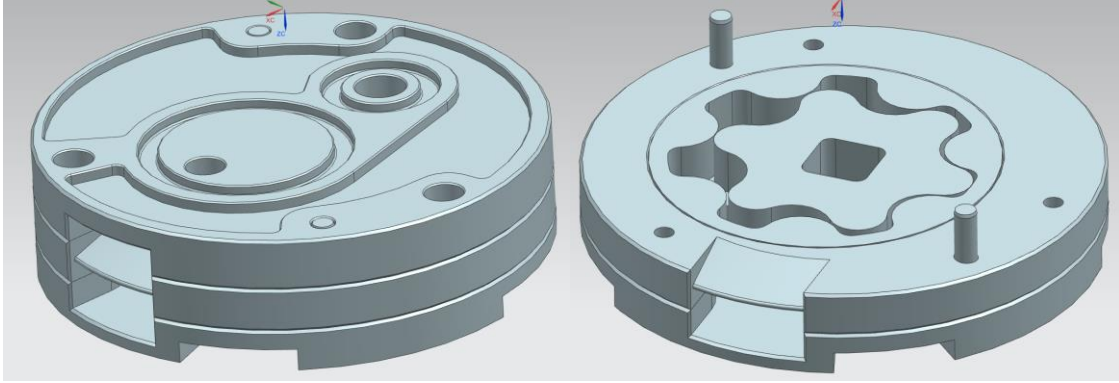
Gerotor pompa patlatılmış montaj görüntüsü
